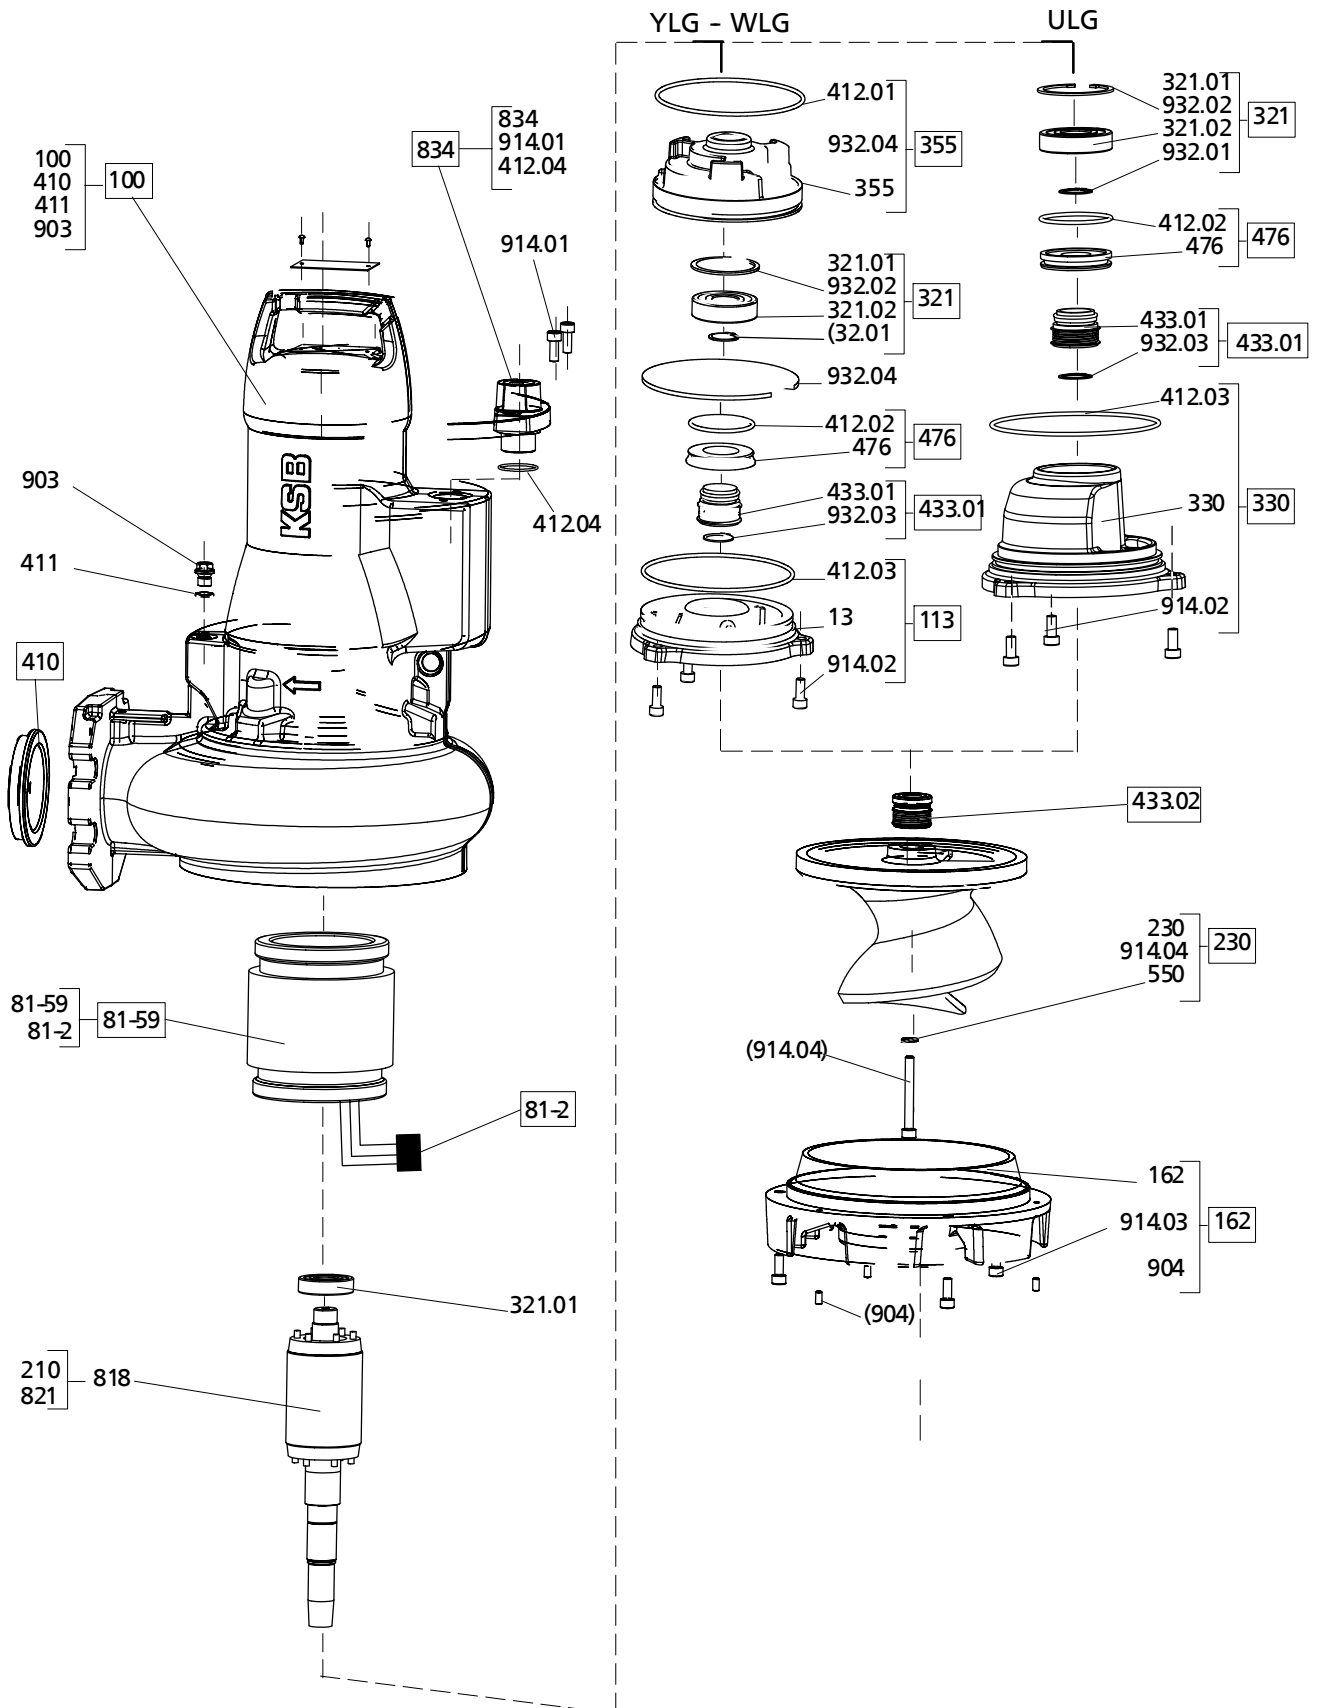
Деталировочный чертеж Amarex N с D 80 - -100
